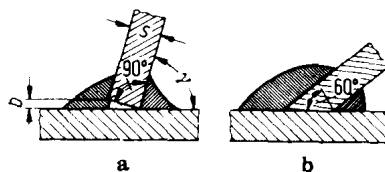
斜接头的角焊缝 a. 坡口未经加工; b. 坡口加工不合理。
